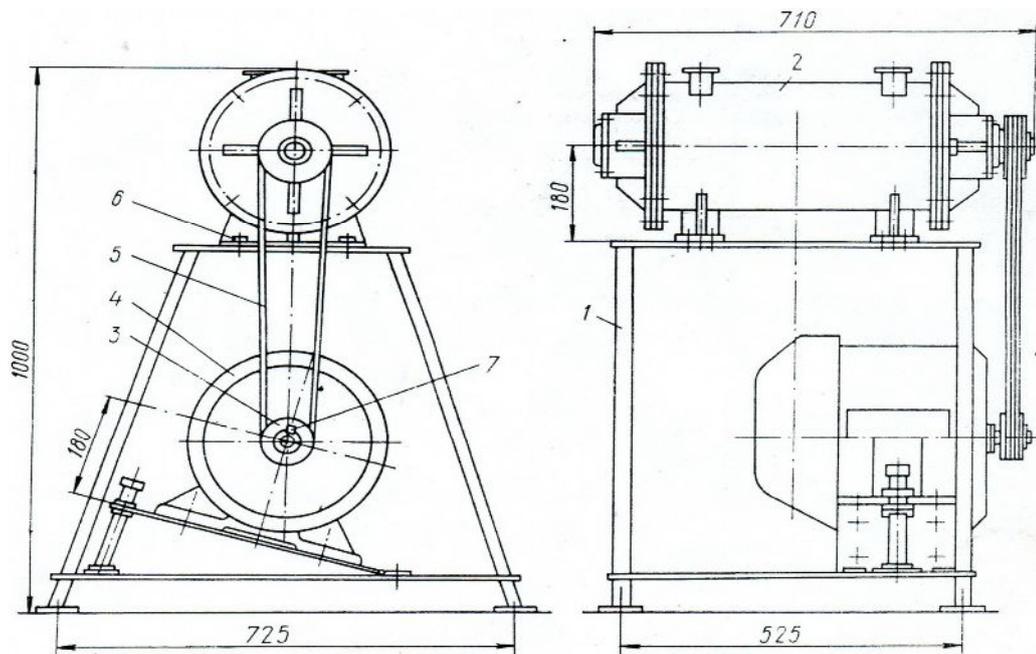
Сборочный чертеж гидромеханического экстрактора:
